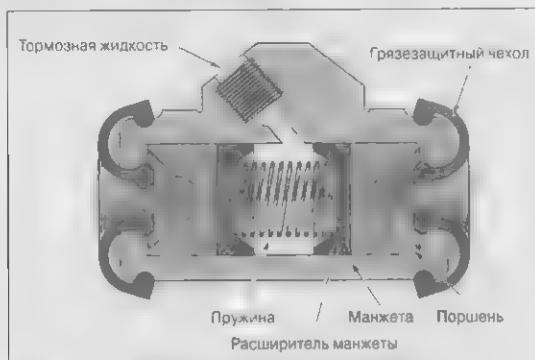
Конструкция рабочего тормозного цилиндра
